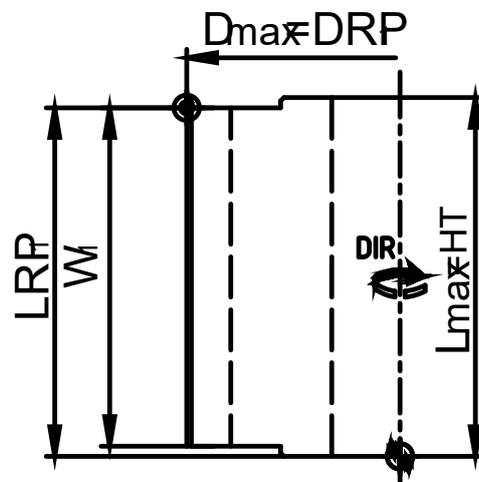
Maßdefinition für Keilzinkenwerkzeuge mit beidseitigen Randzinken
